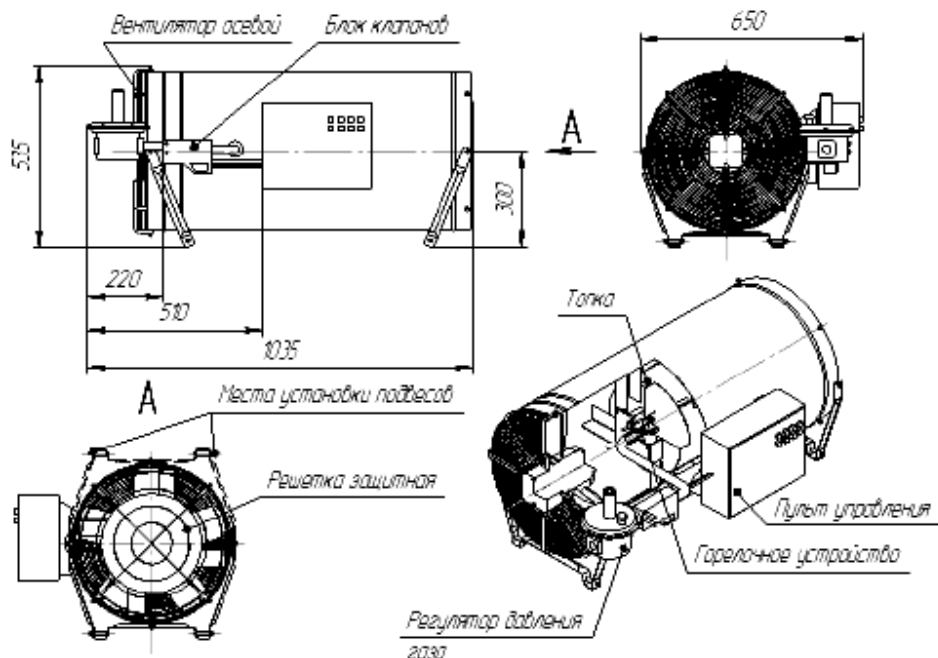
Общий вид воздухонагревателя «Тепловей–170»
